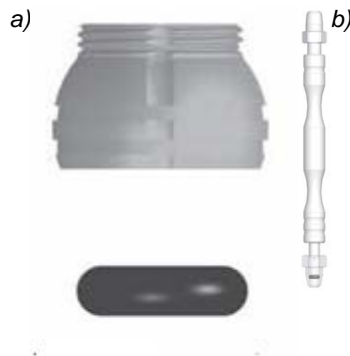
Aditamento O-Ring, a) metal encapsulador y O-ring, b) instrumento para colocar el O-ring dentro del metal encapsulador
